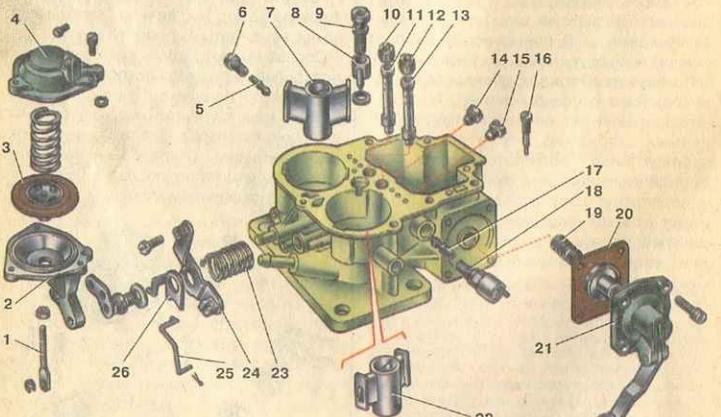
Детали корпуса карбюратора: 1 – шток пневмопривода дроссельной заслонки вторичной камеры; 2 – корпус пневмопривода; 3 – диaphragма; 4 – крышка пневмопривода; 5 – толливный жиклер переходной системы второй камеры; 6 – корпус топливного жиклера переходной системы; 7 – малый диффузор; 8 – распылитель ускорительного насоса; 9 – топливоподводящий винт ускорительного насоса; 10 – главный воздушный жиклер второй камеры; 11 – эмульсионная трубка второй камеры; 12 – главный воздушный жиклер первичной камеры; 13 – эмульсионная трубка первичной камеры; 14 – главный топливный жиклер первичной камеры; 15 – главный топливный жиклер первичной камеры; 16 – регулировочный винт ускорительного насоса; 17 – топливный жиклер холостого хода; 18 – электромагнитный клапан жиклера холостого хода; 19 – возвратная пружина ускорительного насоса; 20 – диaphragма ускорительного насоса; 21 – крышка ускорительного насоса; 22 – малый диффузор первичной камеры; 23 – возвратная пружина рычажного привода воздушной заслонки; 24 – рычаг привода воздушной заслонки; 25 – тяга связи с дроссельной заслонкой; 26 – кронштейн возвратной пружины дроссельных заслонок
